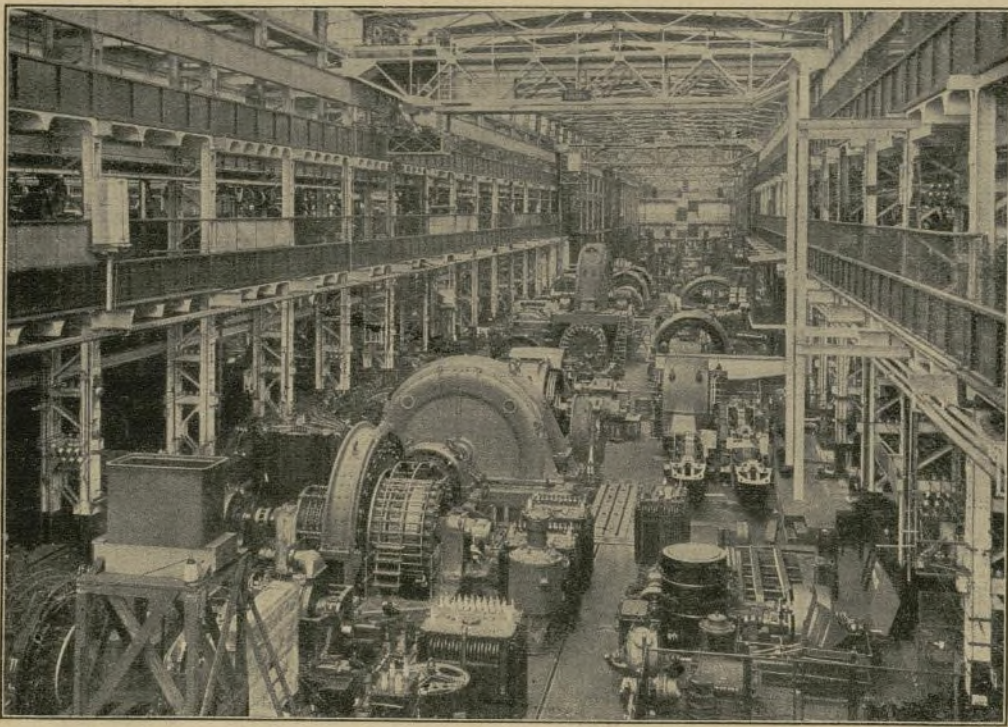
Enorme sala de montaje del taller de dinamos de Siemensstadt.
